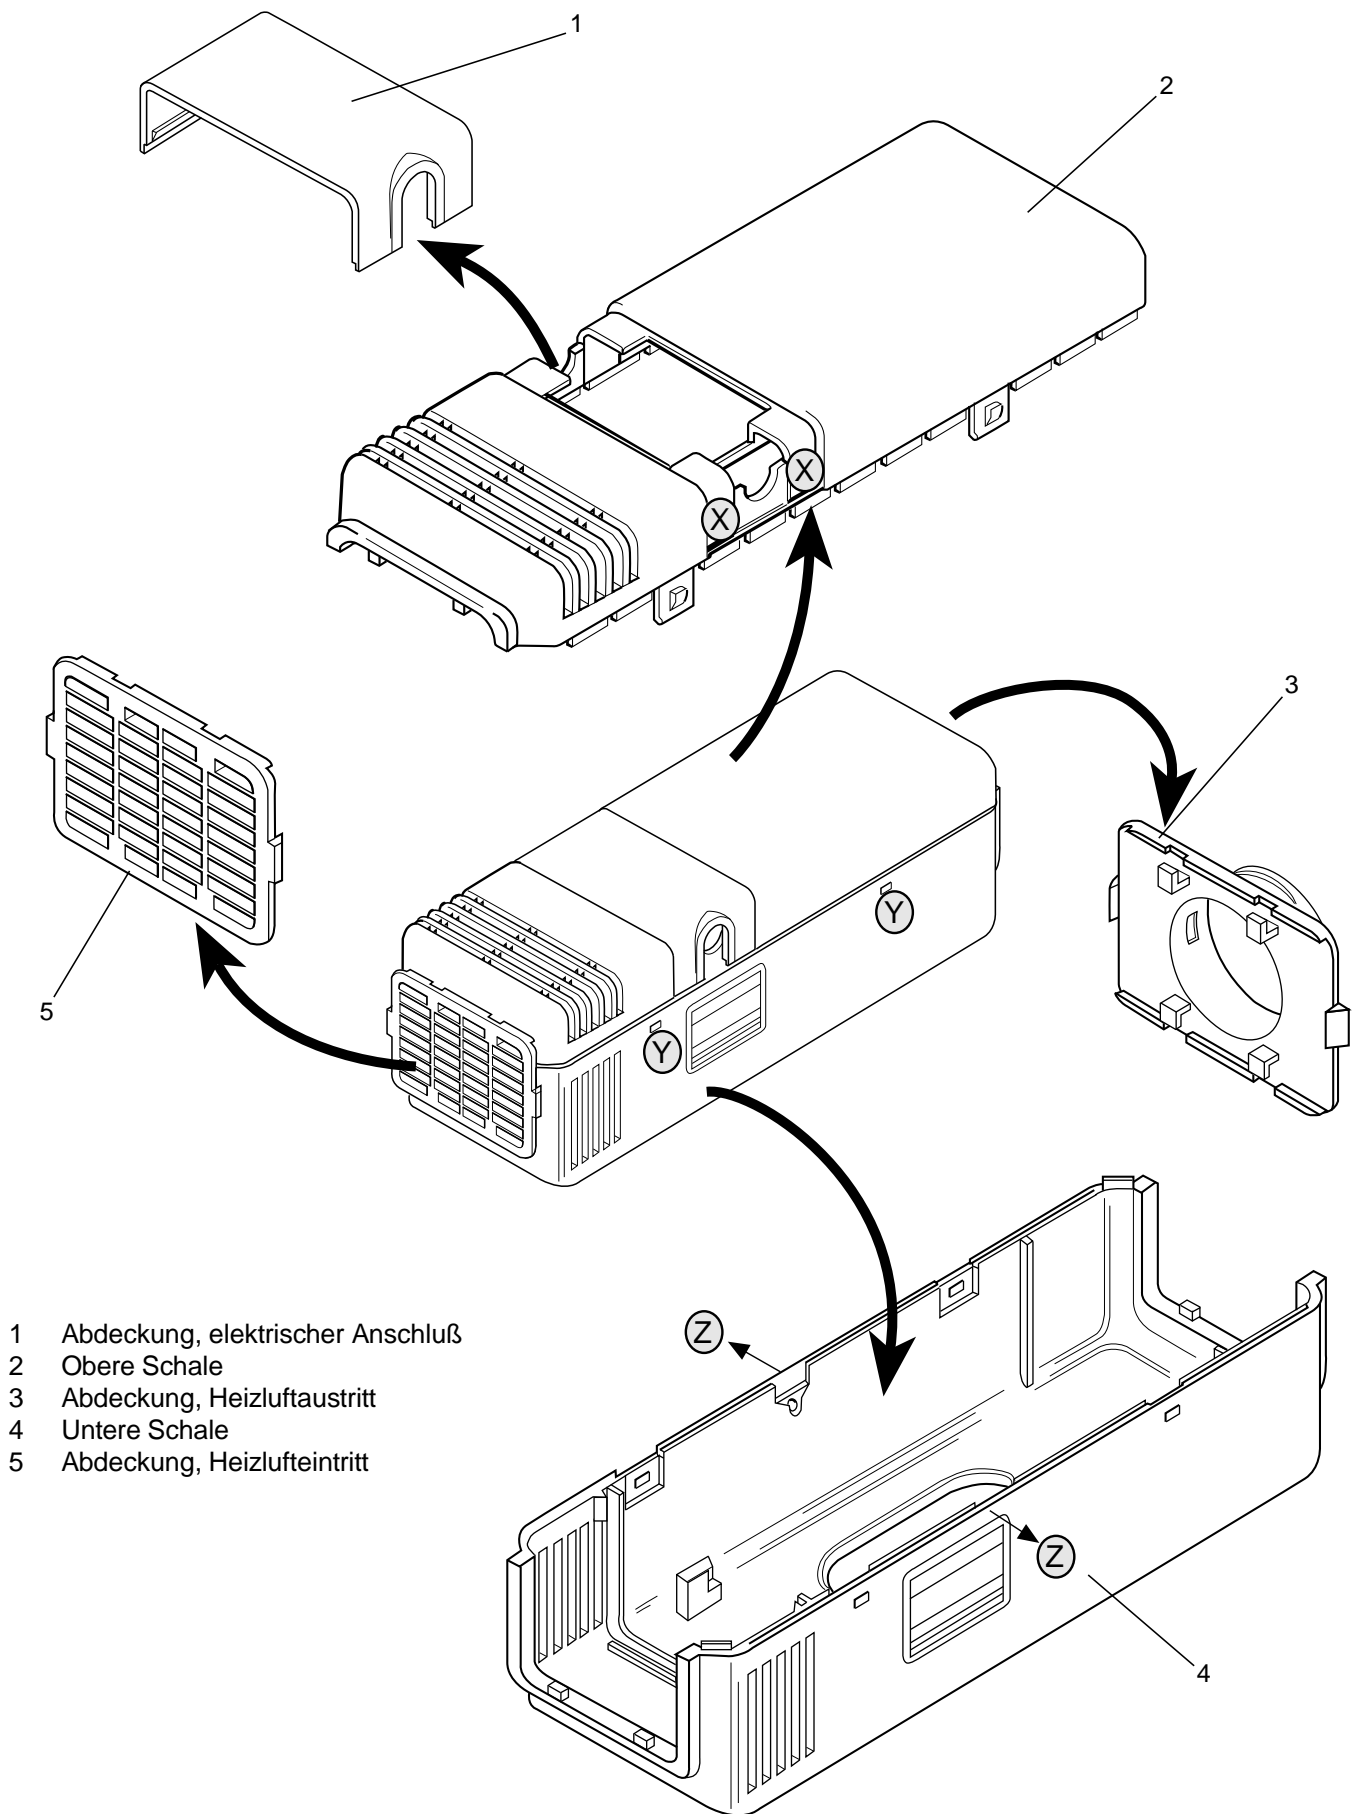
Entfernen der Gehäuseteile/Abdeckungen
